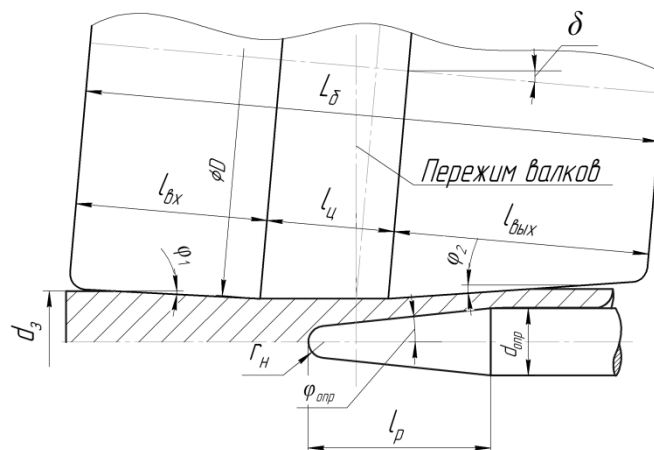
Калибровка рабочего валка и оправки прошивного стана
